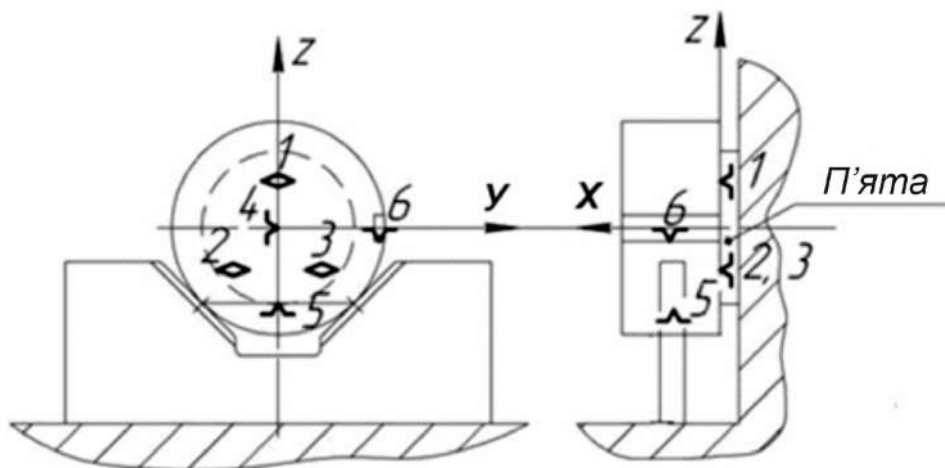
Базування короткої циліндричної заготовки у призмі з фіксацією від повороту
